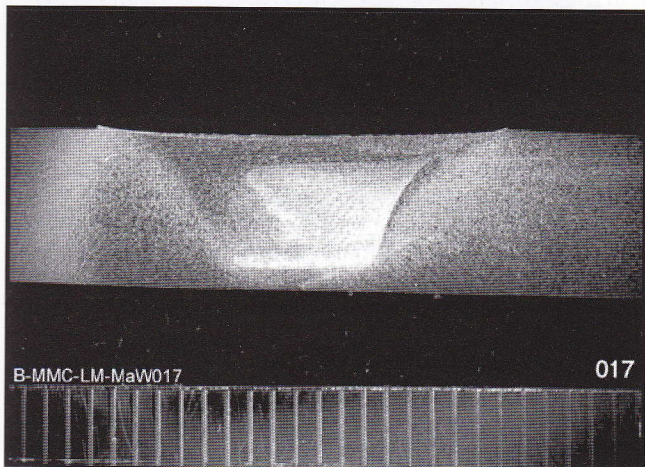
Macrografia della saldatura FSW di Al-CMM, senza attacco chimico
